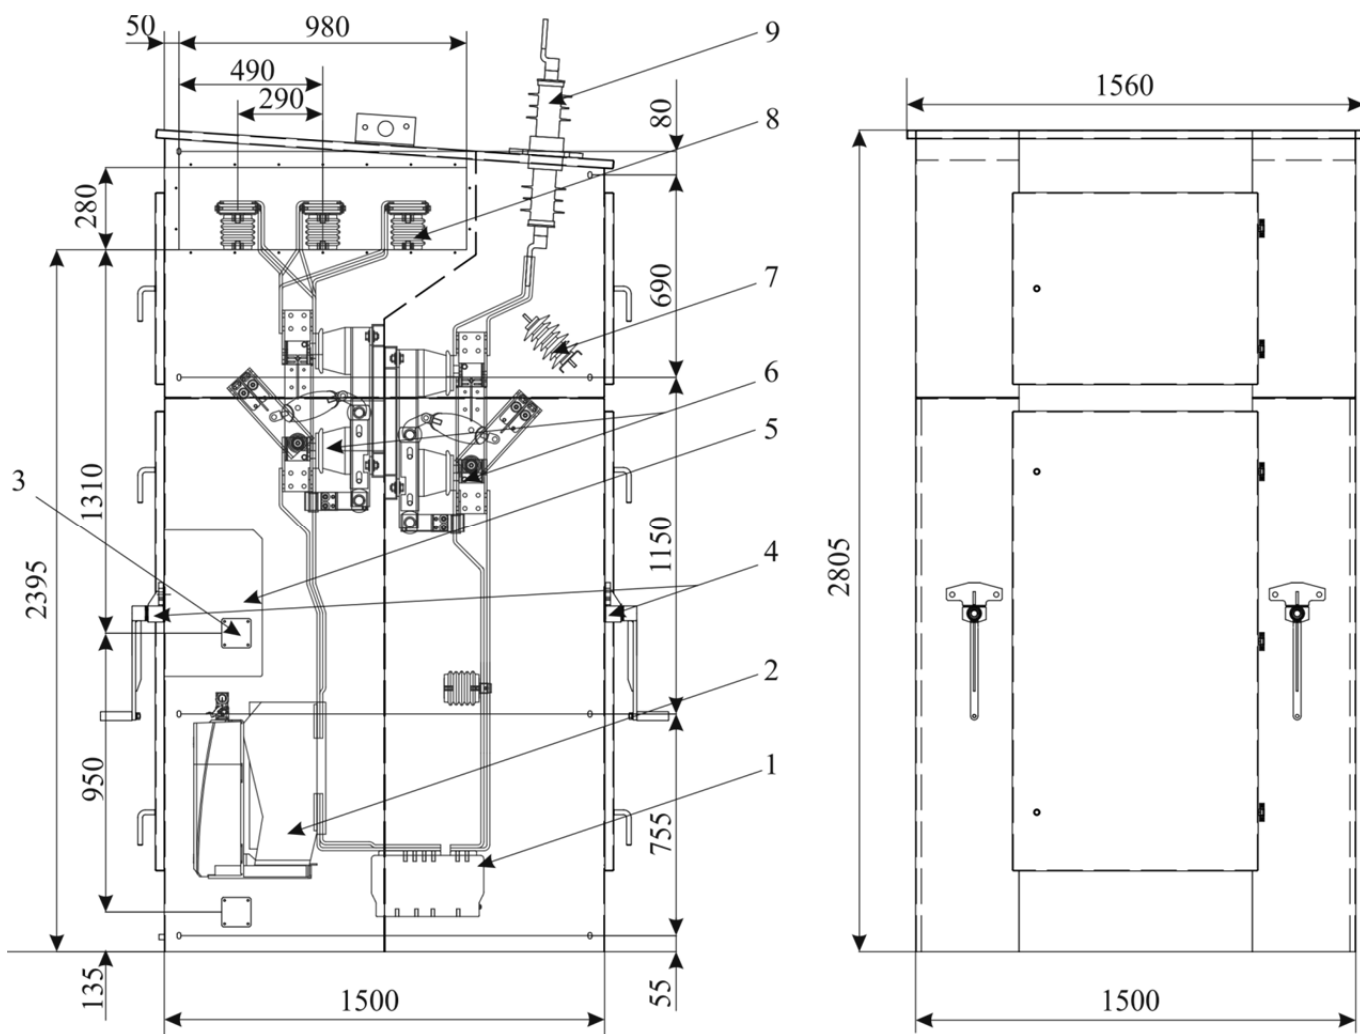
Габаритные размеры и устройство КРН с вакуумным выключателем
